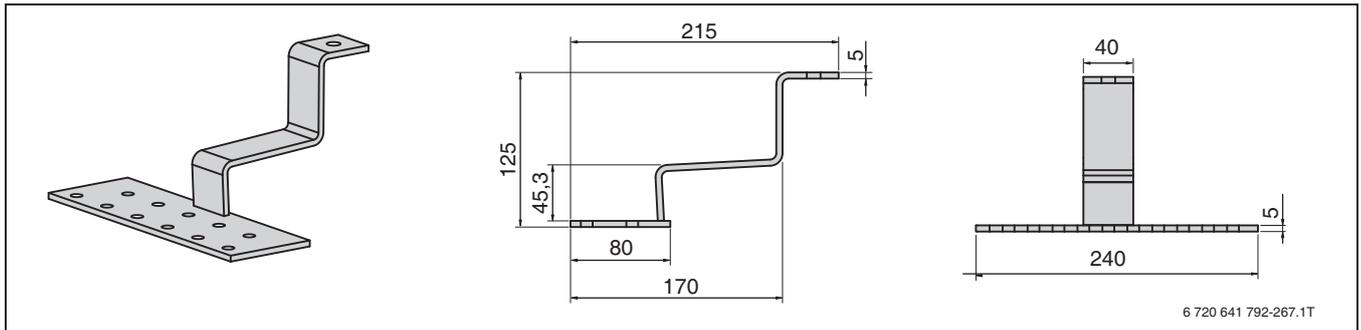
Collegamento da tetto per Logasol SKR con coperture con tegole, tegole in laterizio ed embrici
